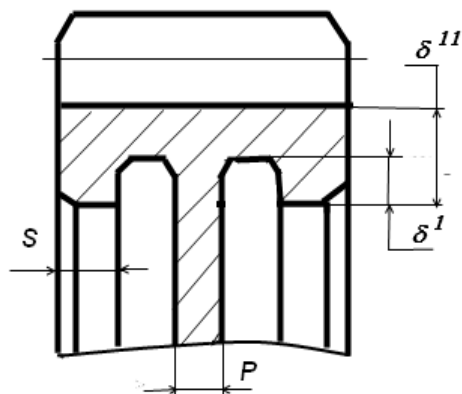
Элементы конструкции венца зубчатого колеса
